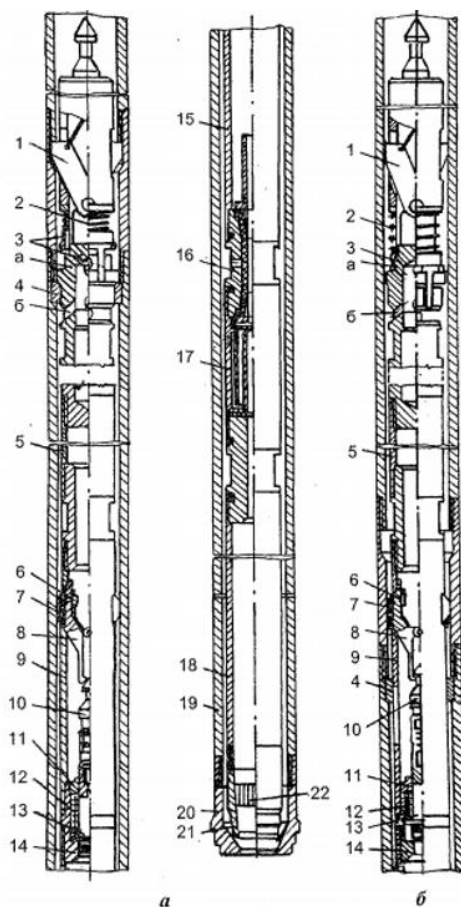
Съемный керногазонаборник СКГН-76А
